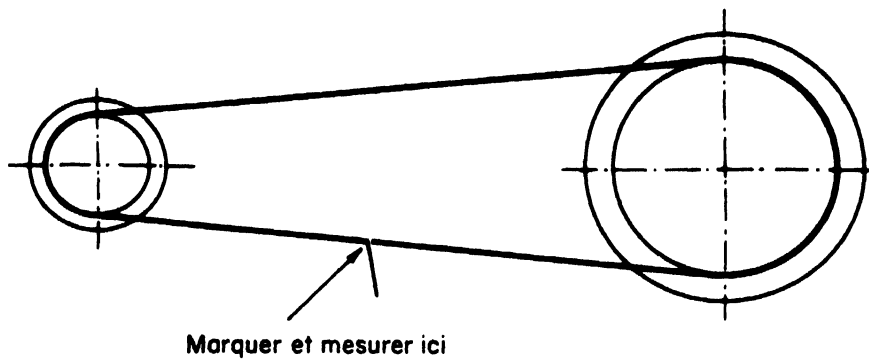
MESURE DE LA LONGUEUR D'UNE COURROIE TRAPEZOIDALE
